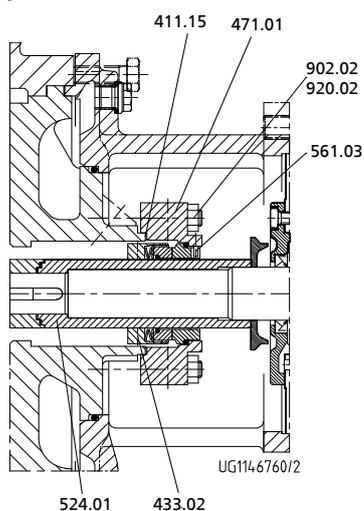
Cierre mecánico con tapa de carcasa cilíndrica
